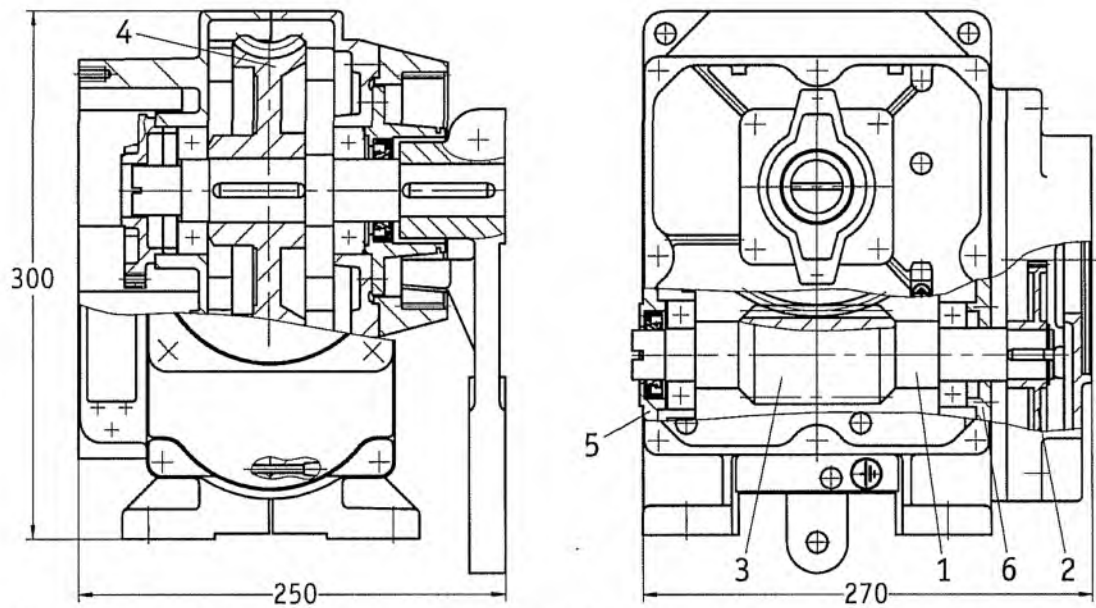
Редуктор фланцевого исполнения с дополнительной передачей механизмов «МЭ0-250» (остальное – см. рис. 8 или 9)
